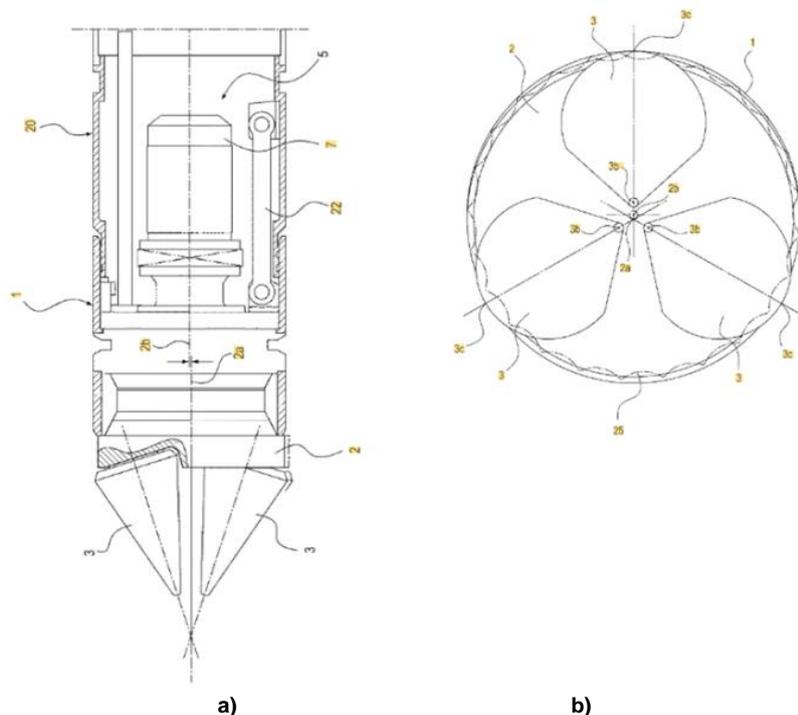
Устройство для вращающегося проникновения: а – вид спереди; б – вид сверху; 1 – защитный корпус; 2 – поворотная головка; 2а – ось вращения; 2б – орбитальная ось; 3 – конусообразный ротор; 3б – верхняя часть; 3с – основание; 5 – приводное устройство; 7 – приводной механизм; 20 – защитный кожух; 22 – планки; 25 – направляющая линия
